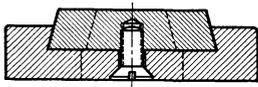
Befestigung der Schnittplatte durch Schwalbenschwanz und Zugschraube.
